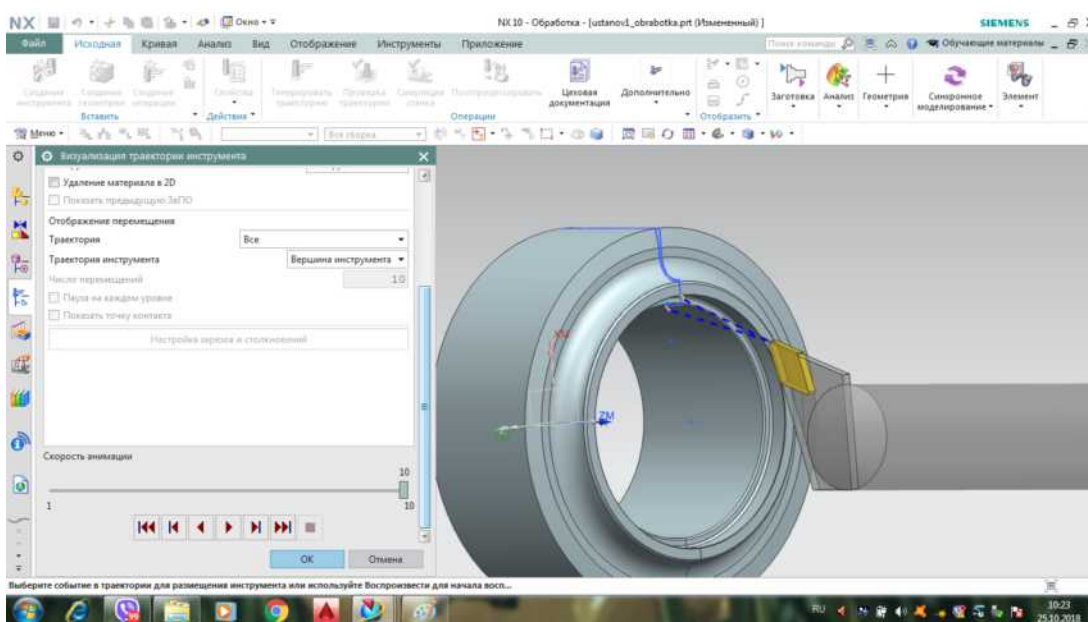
Траекторія обробки з інструментом установка 1, перехід 3
